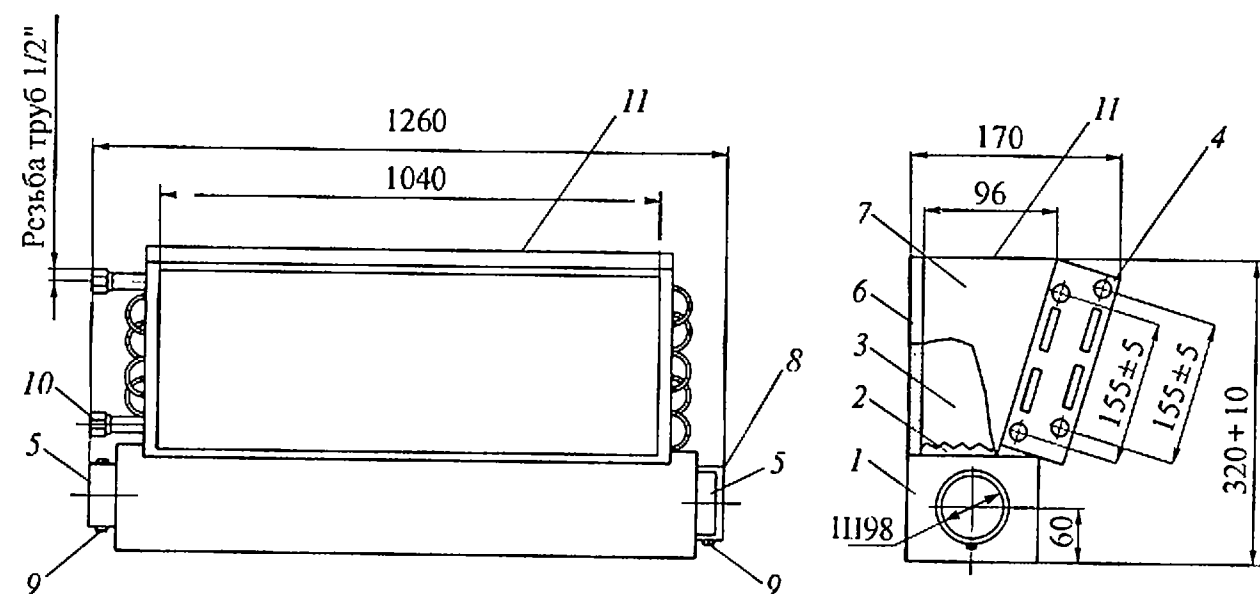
Конструкция доводчика эжекторного ДЭ.2.6.140/180: 1 — камера первичного воздуха; 2 — сопловой элемент; 3 — камера смещения; 4 — теплообменник; 5 — патрубок; 6 — задняя стенка; 7 — боковые стенки; 8 — заглушка; 9 — хомут; 10 — транспортная пробка; 11 — выходное сечение
